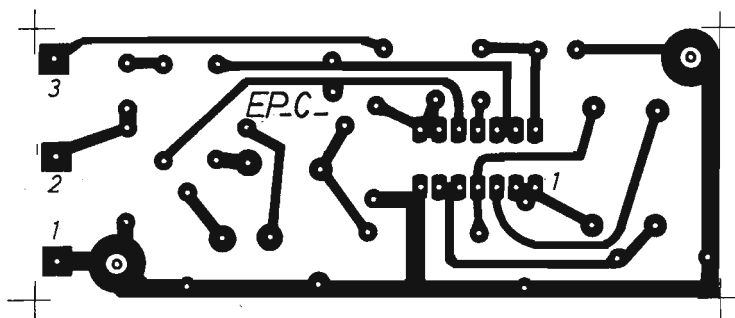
Disegno in grandezza reale del circuito stampato sul quale si compone il progetto della sirena elettronica.
